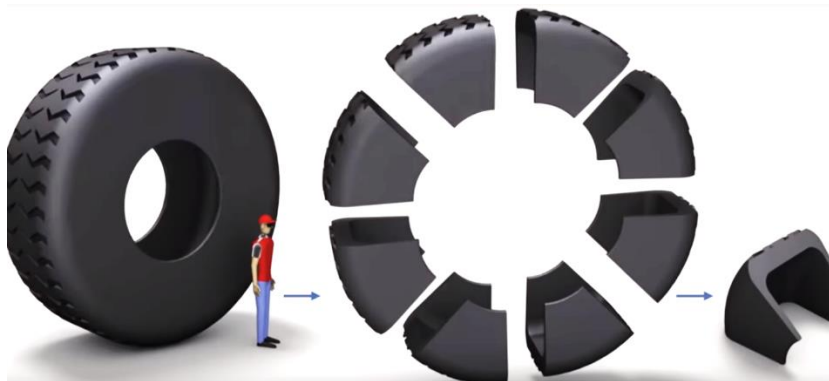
Reducción de dimensiones por corte de llantas OTR
